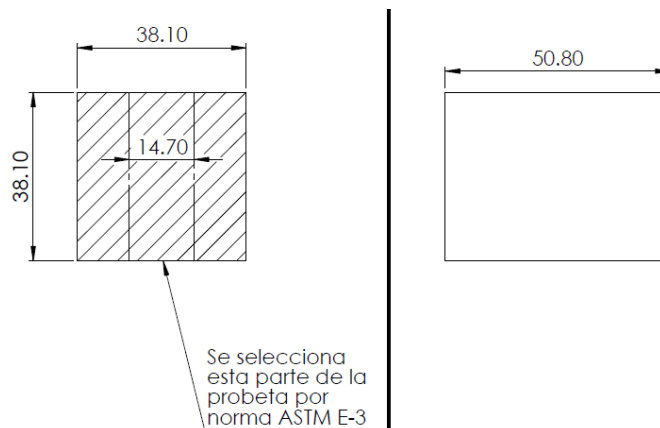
Dimensiones de la probeta a rellenar con soldadura.
